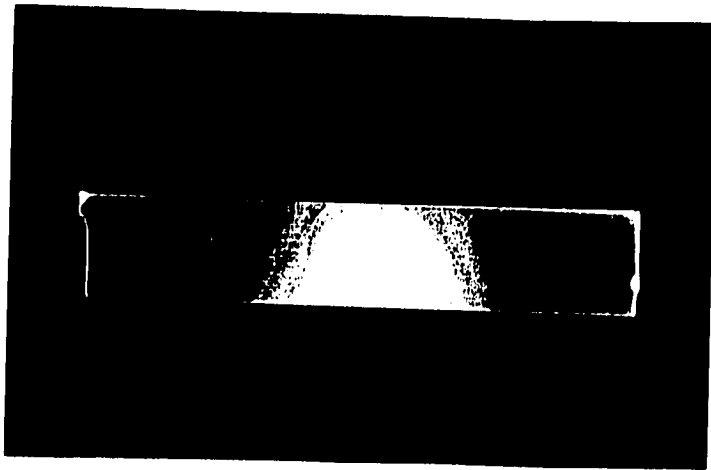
Macrografía de la zona de la soldadura en un acero AISI- 1025 utilizando el fúndente comercial
